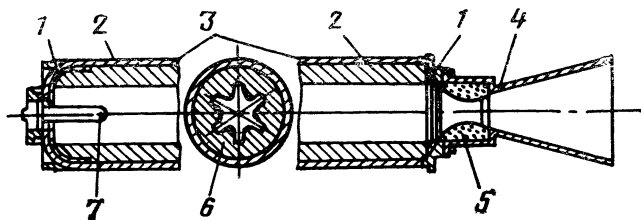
Схема ракетного двигателя на твердом топливе:
